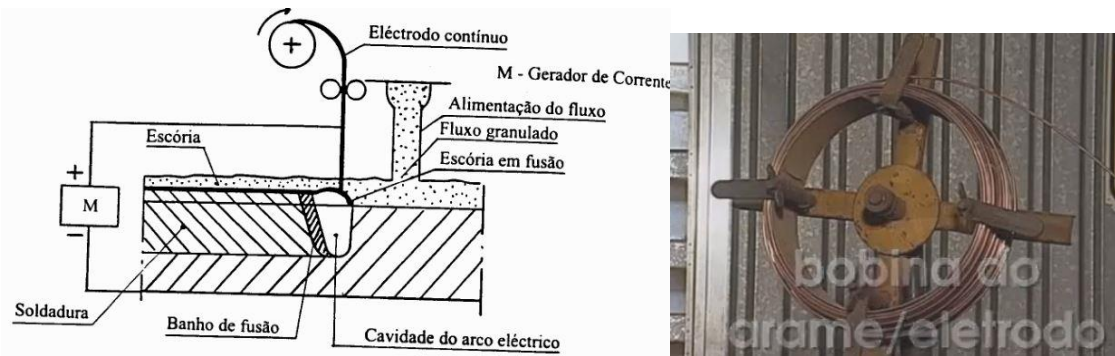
À esquerda, representação da soldadura por arco submerso, à dª. a bobina que tem o arame eletrodo que também é o metal de adição.
